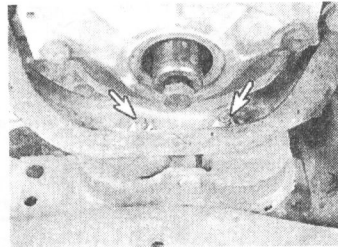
Для отсоединения двигателя от подрамника вывернуть 2 гайки (показаны стрелками) подушки двигателя, находящейся под кожухом цепи газораспределения.
